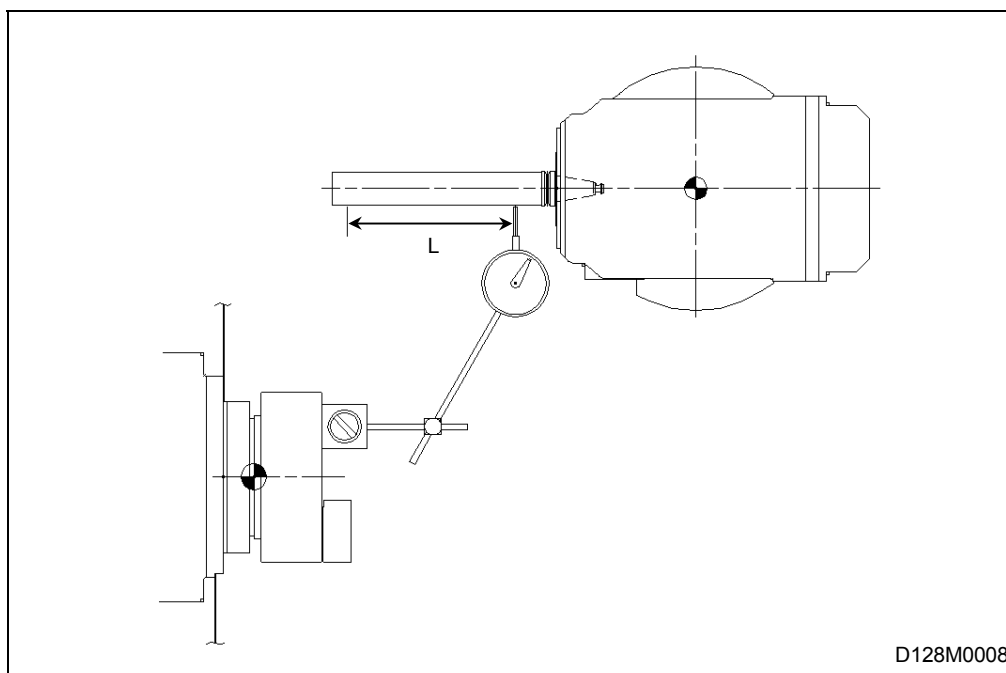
Ось поворота фрезерного шпинделя (ось В)
